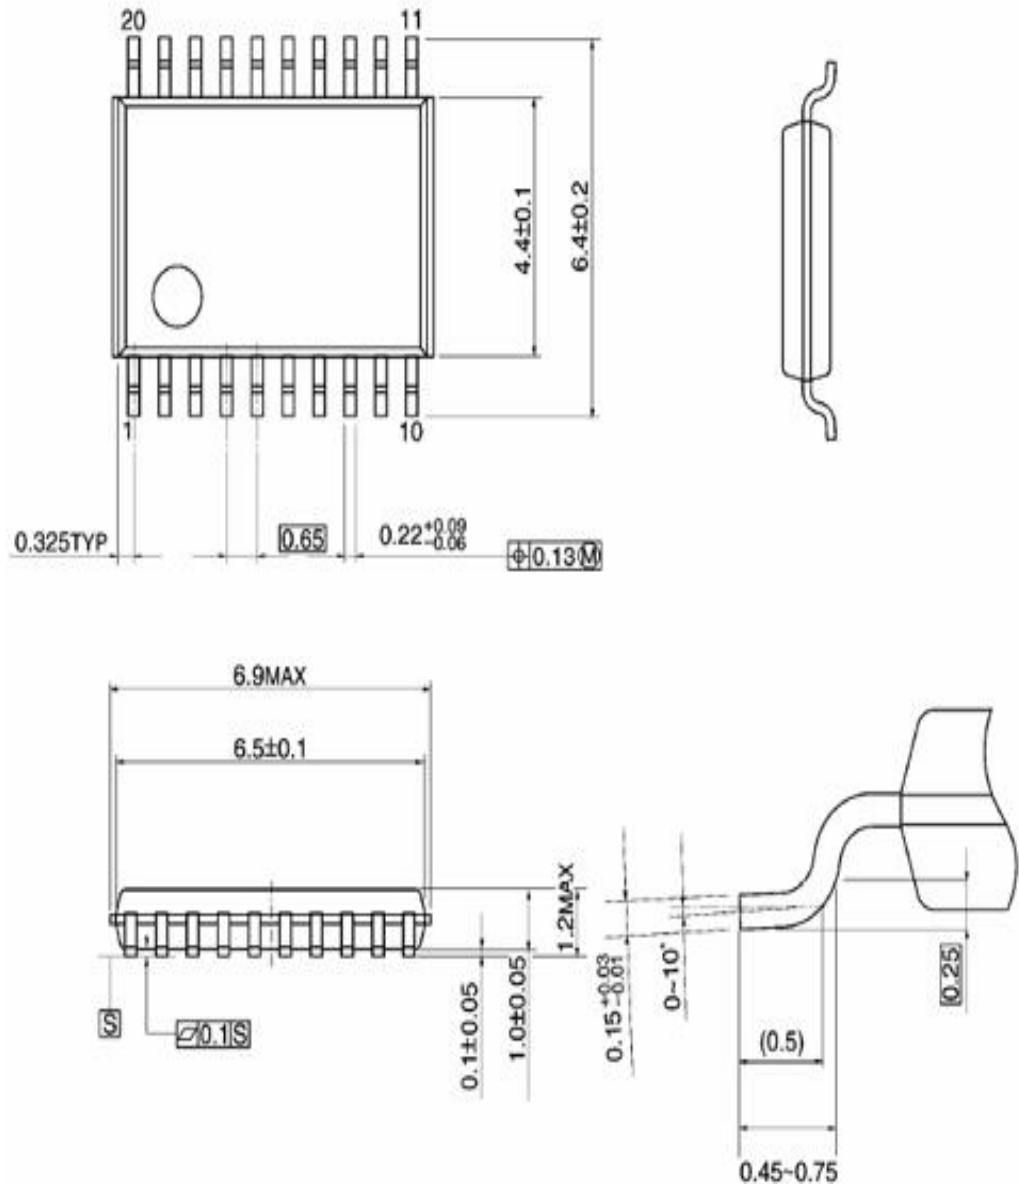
Габаритні розміри мікроконтролера STM8S103F3P6
